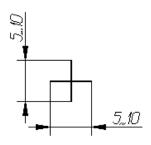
Условное изображение одиночной сварной точки
